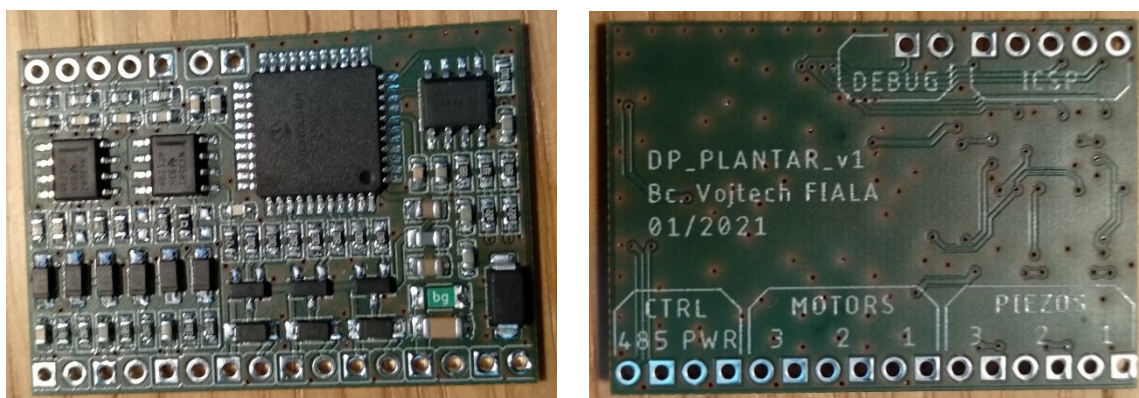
Náhled a layout spodní (bottom) strany platární DPS
